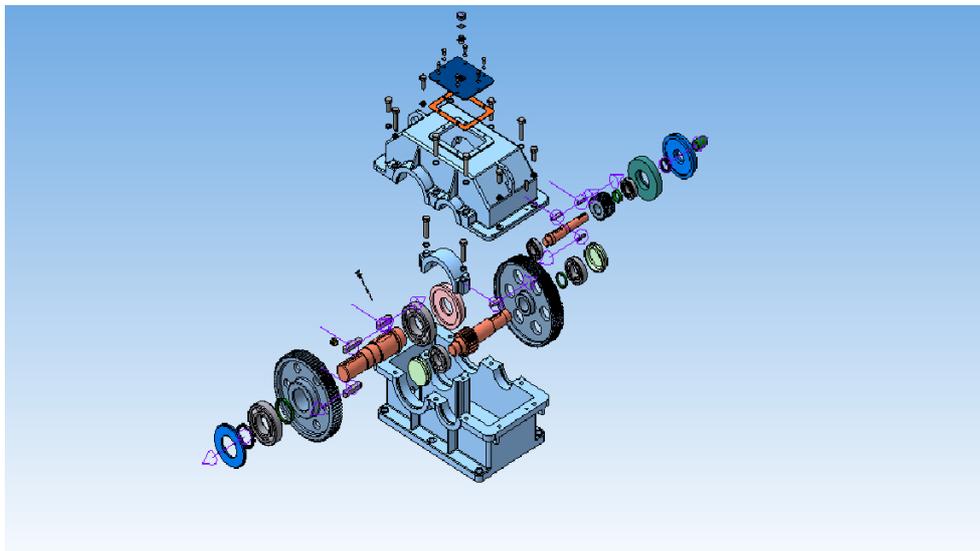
3D модель двухступенчатого цилиндрического соосного редуктора
